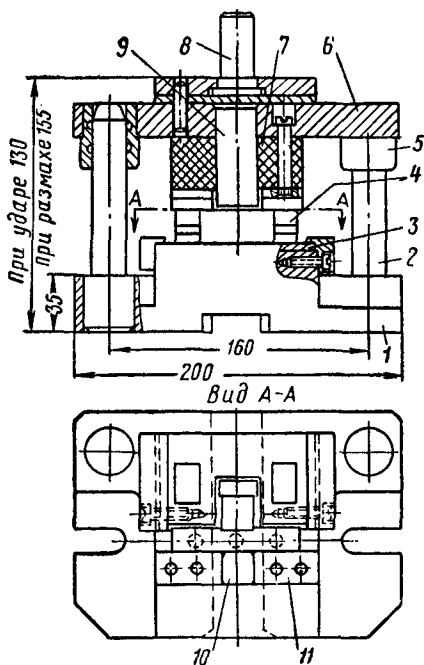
Штамп для обрубки напльвов после сварки шин катушек якоря двигателя ДК-106:
